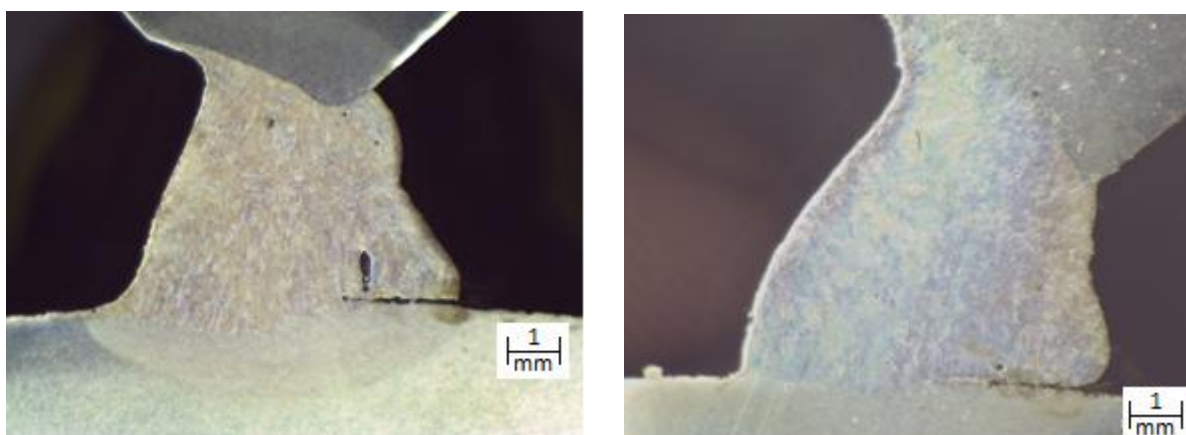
Macrografias de corpos de prova soldados com o gap utilizado atualmente
